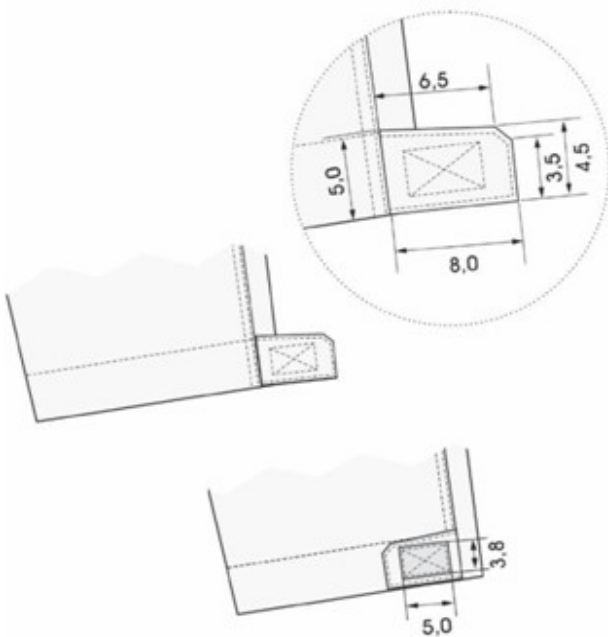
Detalhes da aleta de ajuste da barra da calça (frente)
